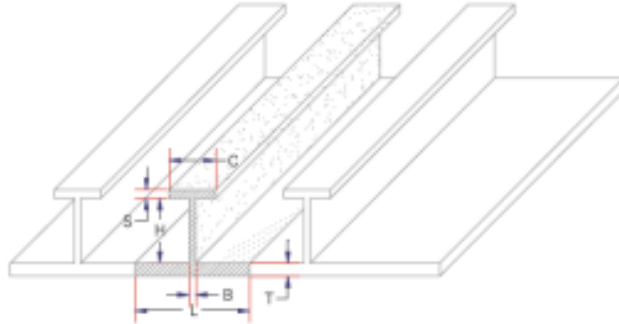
Sección Hidráulica tubería Rib Loc 1,200mm.
